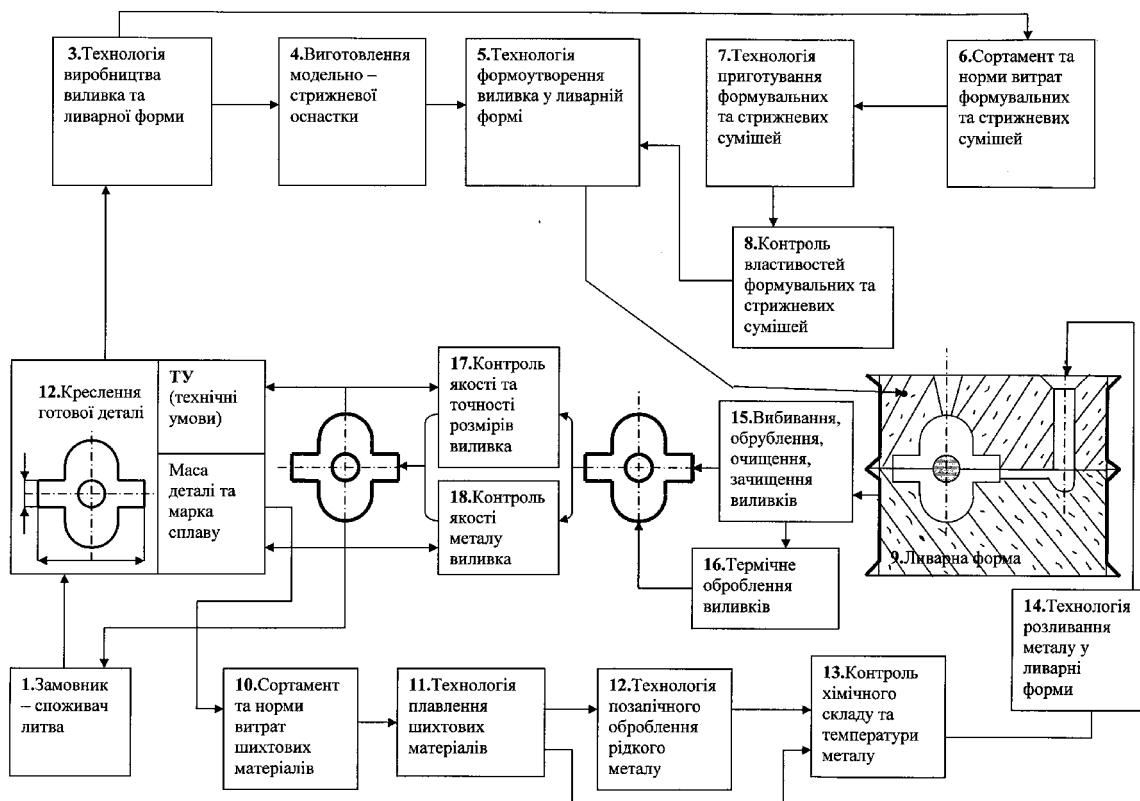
Схема технологічного процесу виготовлення виливка
